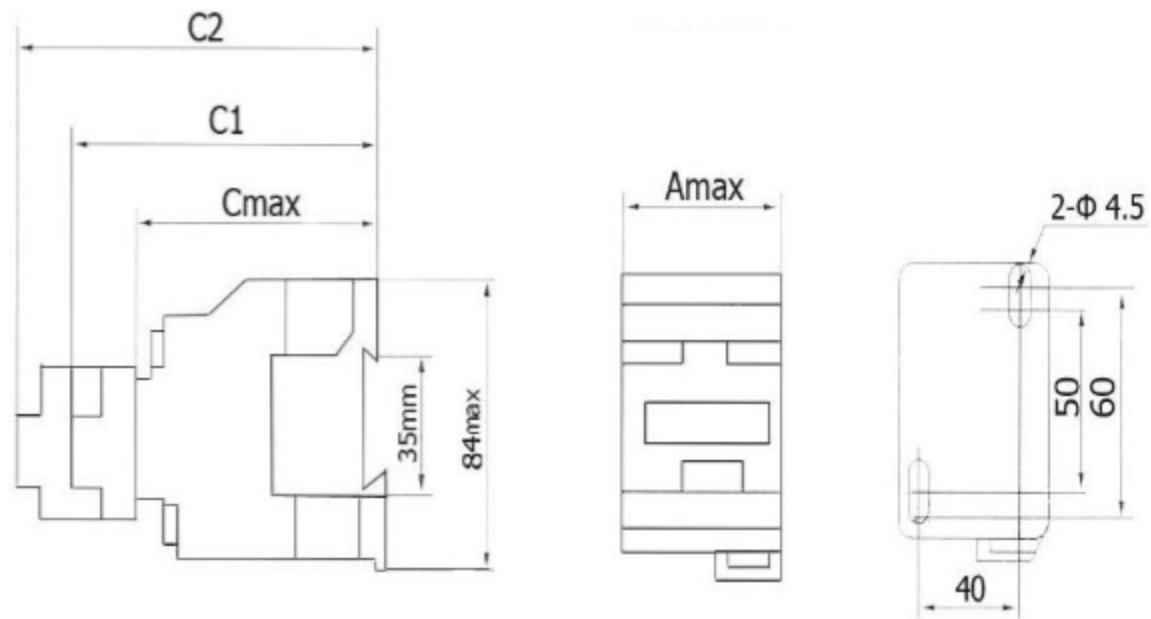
Габаритные и присоединительные размеры пускателей 16-40А
